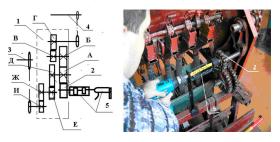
Схема присоединения устройства к редуктору сеялки: 1 – редуктор зерновой сеялки; 2 – зубчатка устройства; вал зерновых аппаратов; 4 – вал туковысевающих аппаратов; 5 — разработанное устройство привода; А — зубчатка редуктора, установленная на его первичном вале
